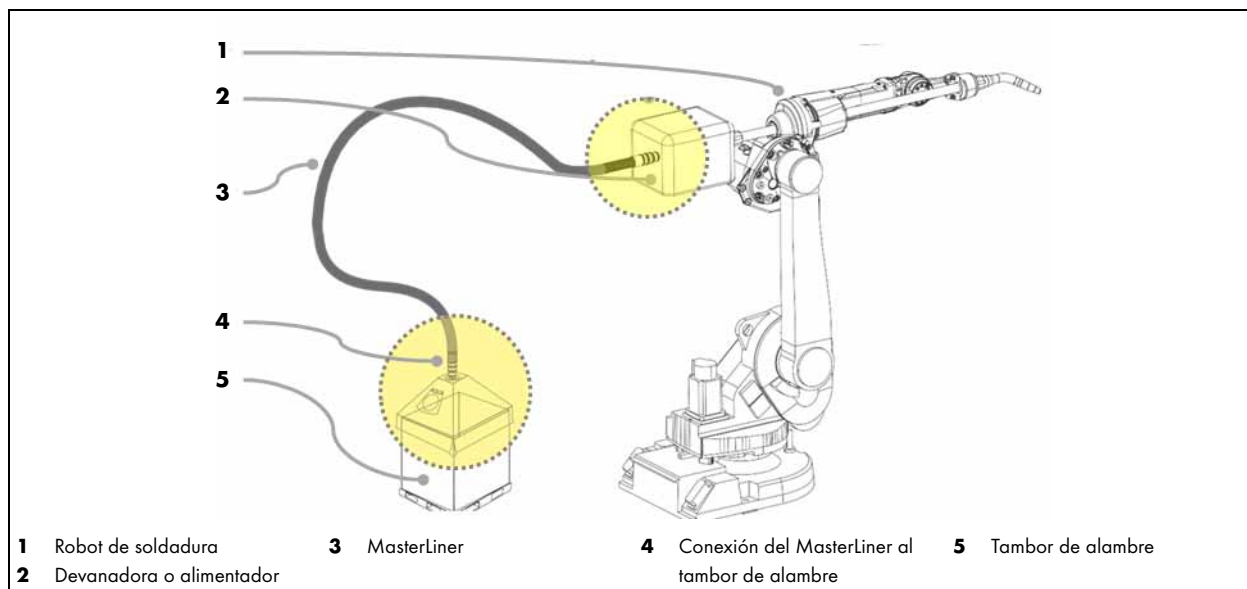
Tendido de la célula de soldadura robotizada
